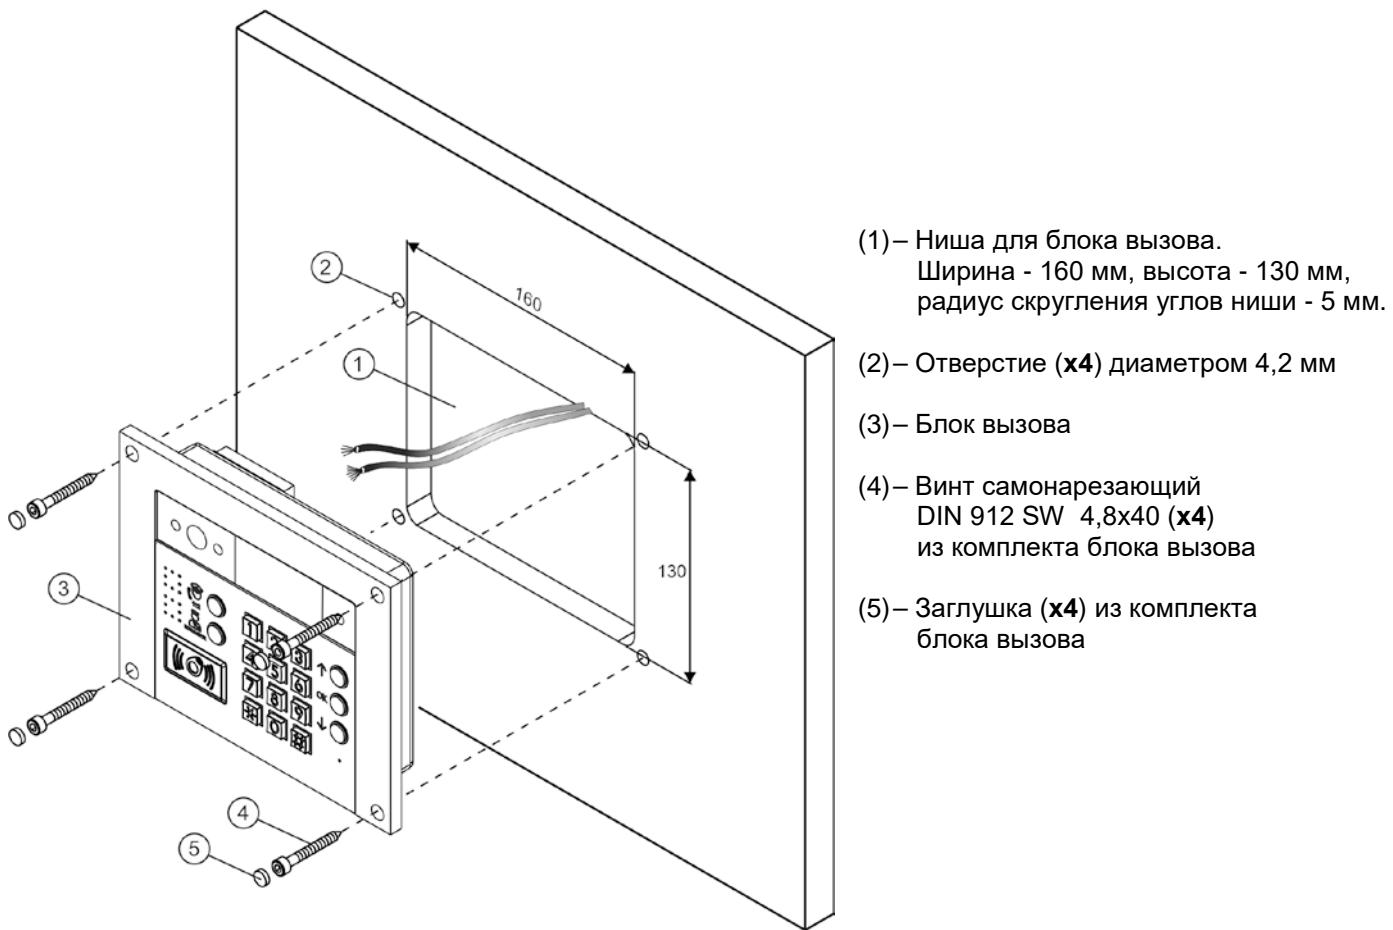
Крепление блока вызова на неподвижную часть металлической двери
